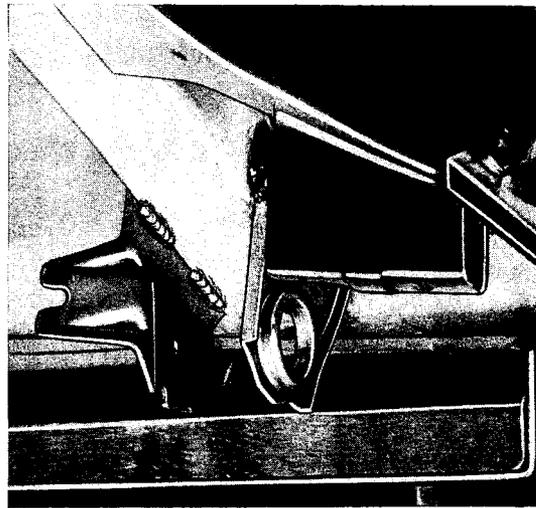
Hinterfederstützen an Unterseite des Hinterlängsträgers lichtbogengeschweißt – Bild zeigt Schweißstellen an innerer Stütze
